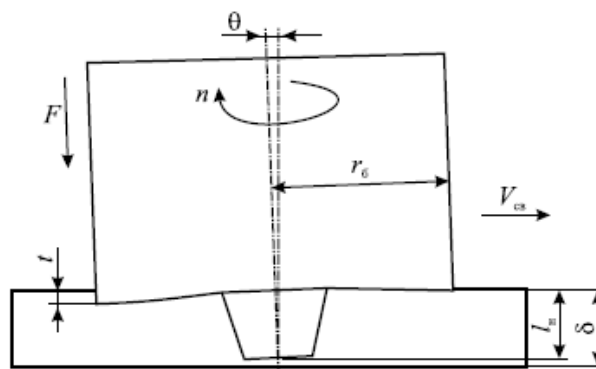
Основные параметры сварки трением с перемешиванием [25].
